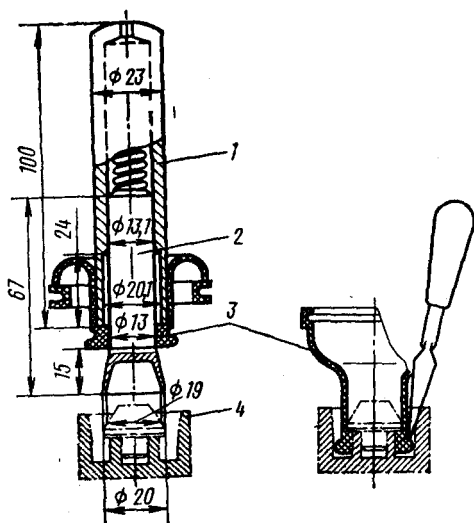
Приспособление для замены колпака колесного цилиндра:
